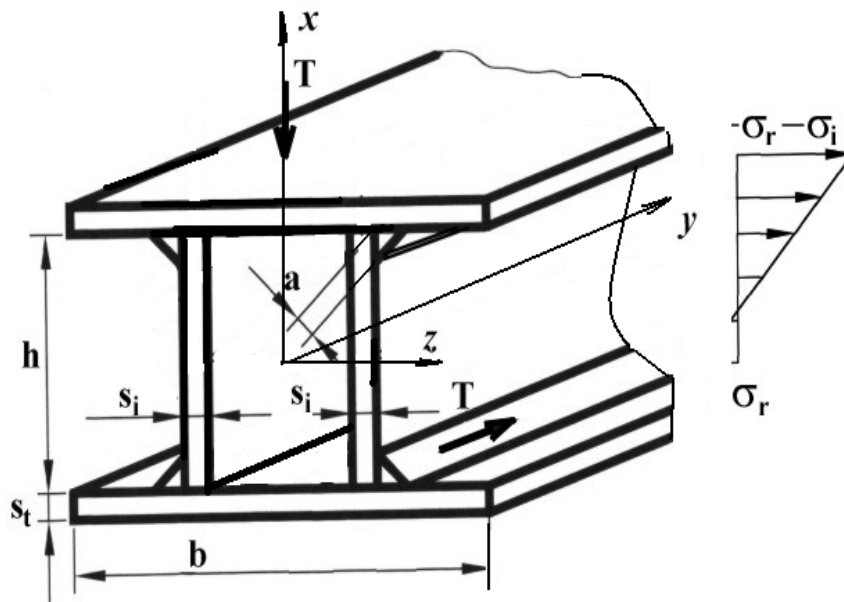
Efecto de corte en los cordones soldadas
